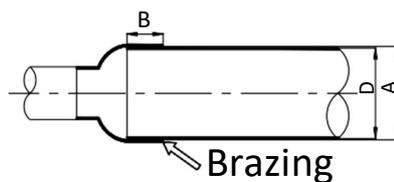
Rohrausrichtung beim Schweißen
